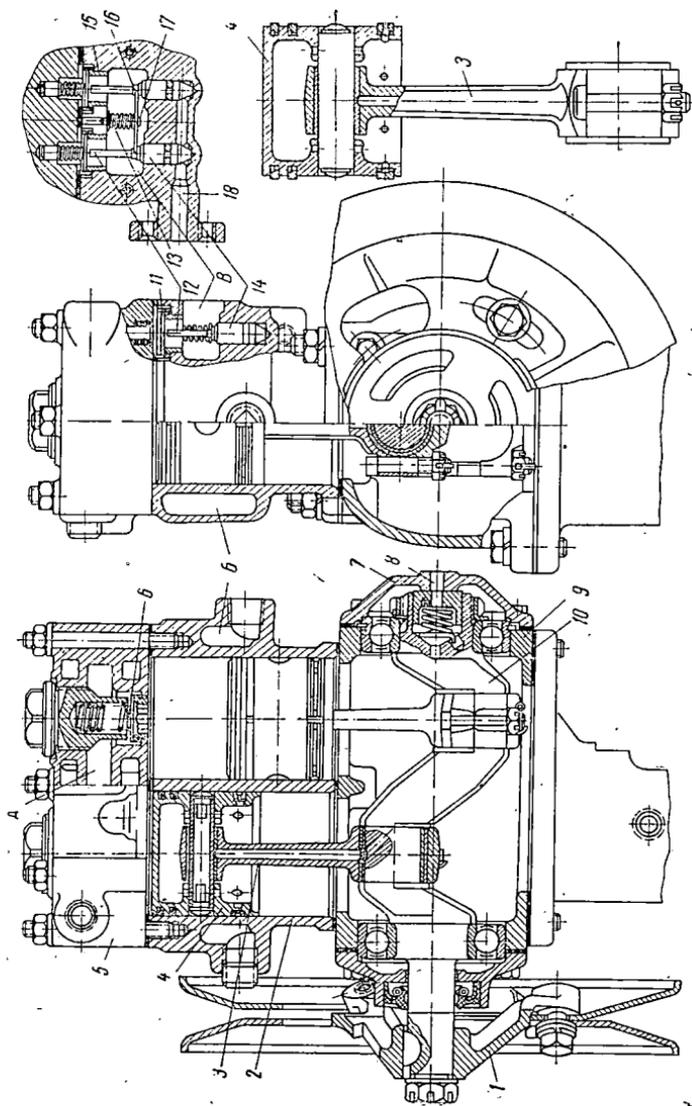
Компрессор (ЗИЛ-130, МАЗ-500, Урал-375):
